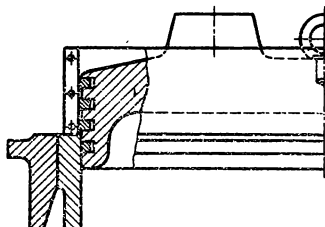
Приспособление для ввода колец в цилиндр, изготовленное из листовой стали толщиной 1,5 мм
